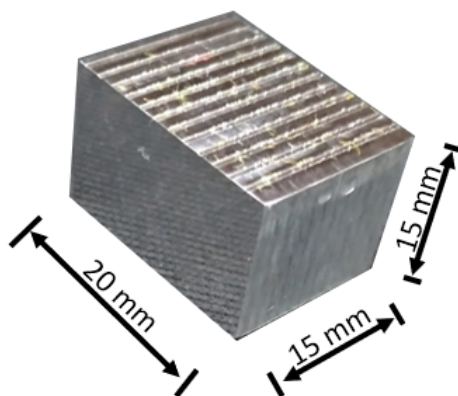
Dimensões e geometria das amostras de Inconel 718.
